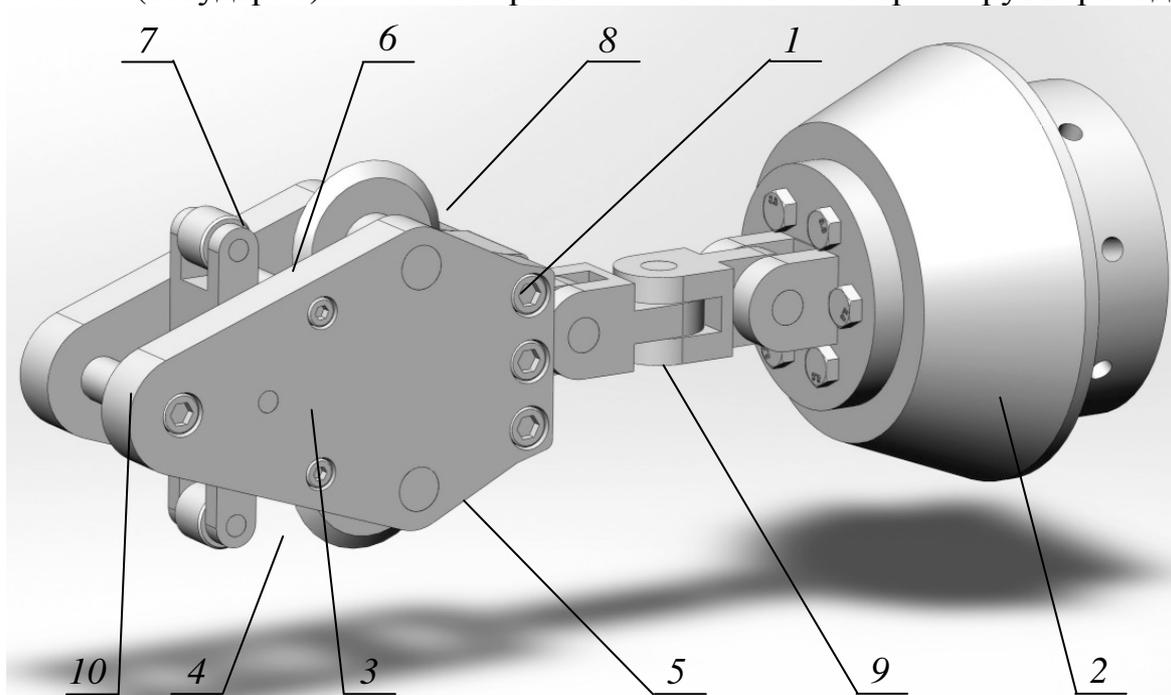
Модель рабочего механизма для бестраншейного ремонта трубопроводов, имеющих изгибы и повороты: 1 – режущая головка; 2 – расширитель для увеличения диаметра скважины; 3–5 – оси; 6 – двулучный рычаг; 7 – опорный каток; 8 – дисковый нож; 9 – шарнир; 10 – крепление.
